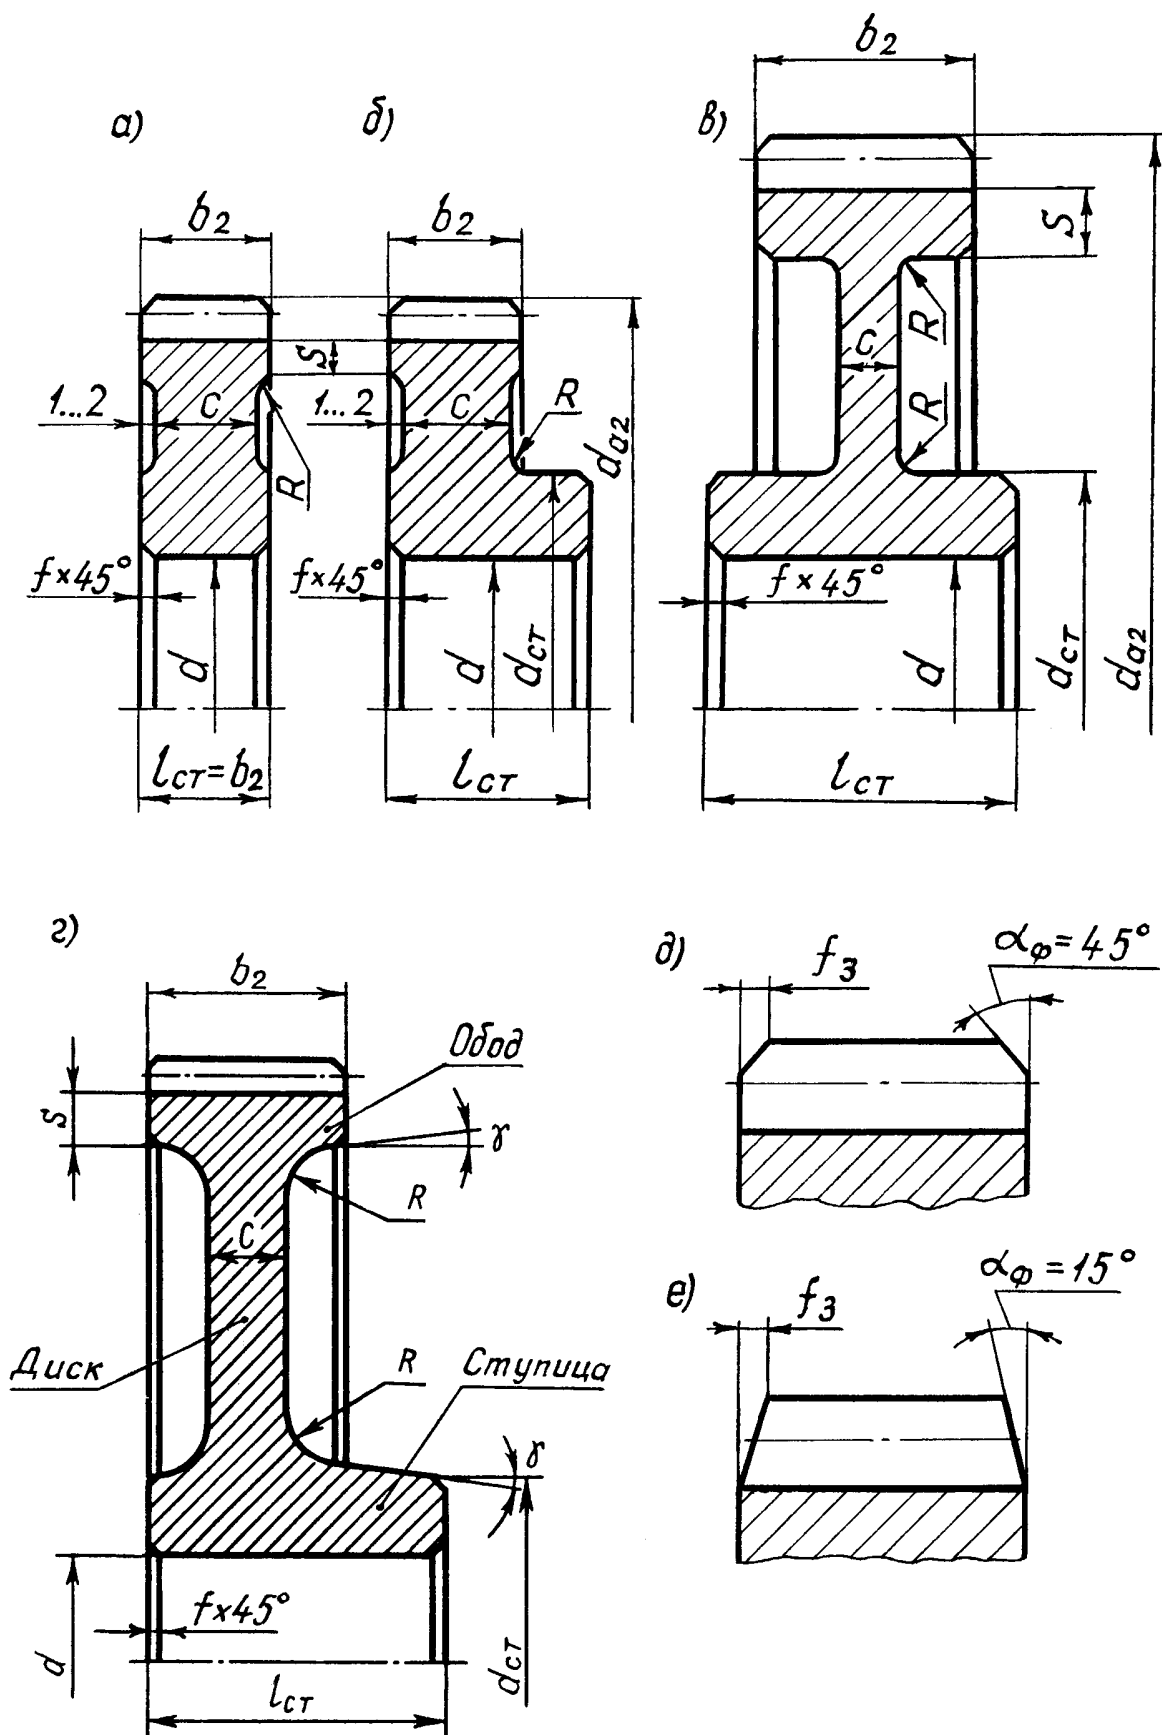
Конструкция цилиндрических зубчатых колес (насадные колеса) [3]
